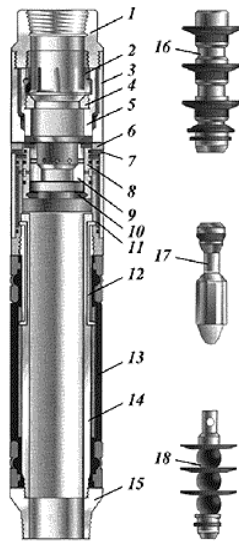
Заколонный гидравлический пакер типа ПДМ для ступенчатого и манжетного цементирования скважин: 1 — переводник верхний; 2 — втулка защитная; 3 — корпус патрубка; 4 — седло верхнее; 5 — втулка верхняя; 6 — отверстие циркуляционное; 7 — винт срезной; 8 — втулка нижняя (верхняя); 9 — седло нижнее; 10 — кольцо упорное; 11 — канал корпуса впускной; 12 — канал осевой; 13 — уплотнитель рукавный; 14 — патрубок уплотнителя; 15 — переводник нижний; 16 — пробка запорная; 17 — пробка падающая; 18 — пробка продавочная
